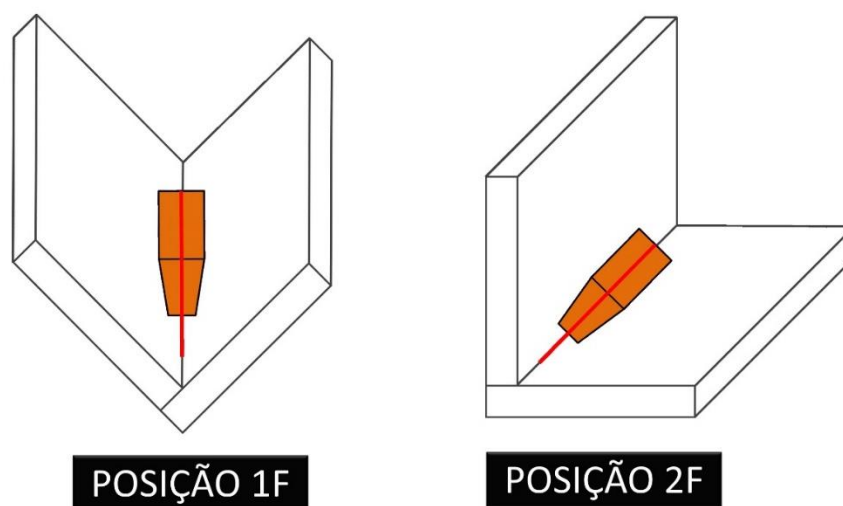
Ilustração das posições de soldagem 1F e 2F para juntas de ângulo.
